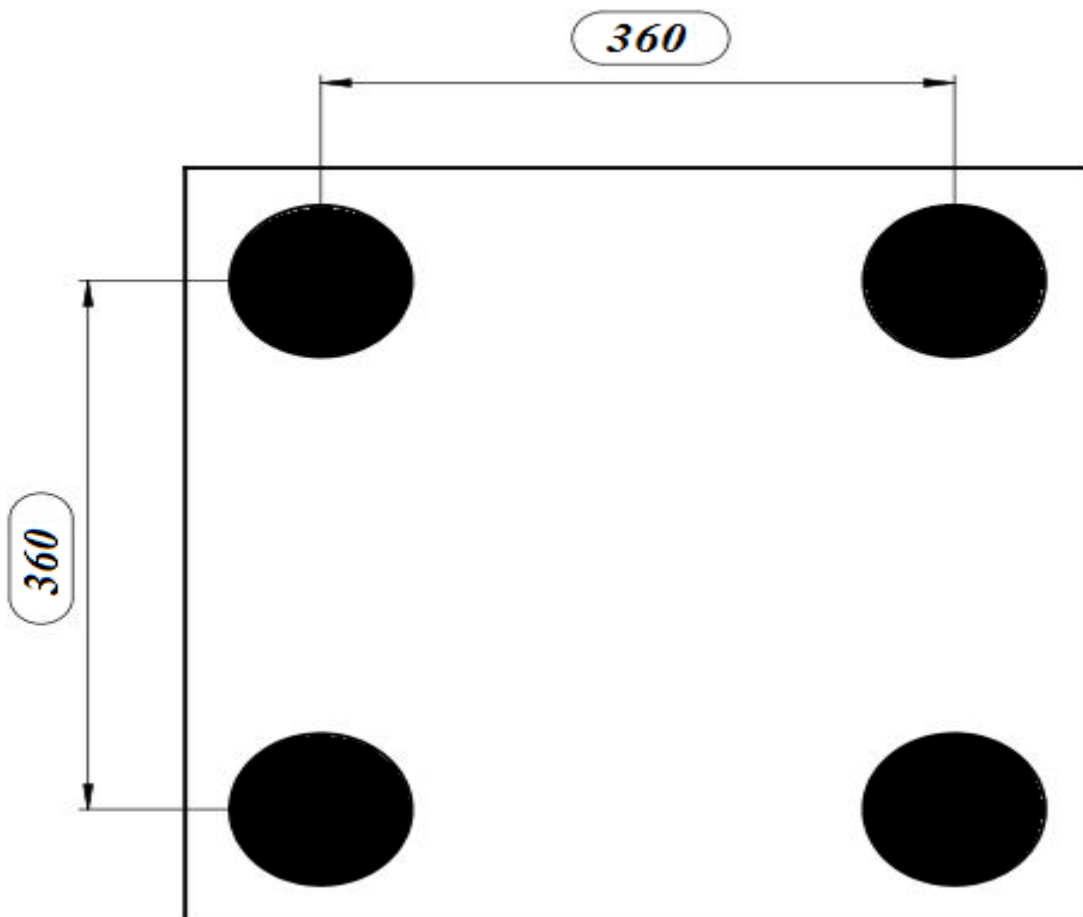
Schémas d'un plateau d'une presse 75T.
